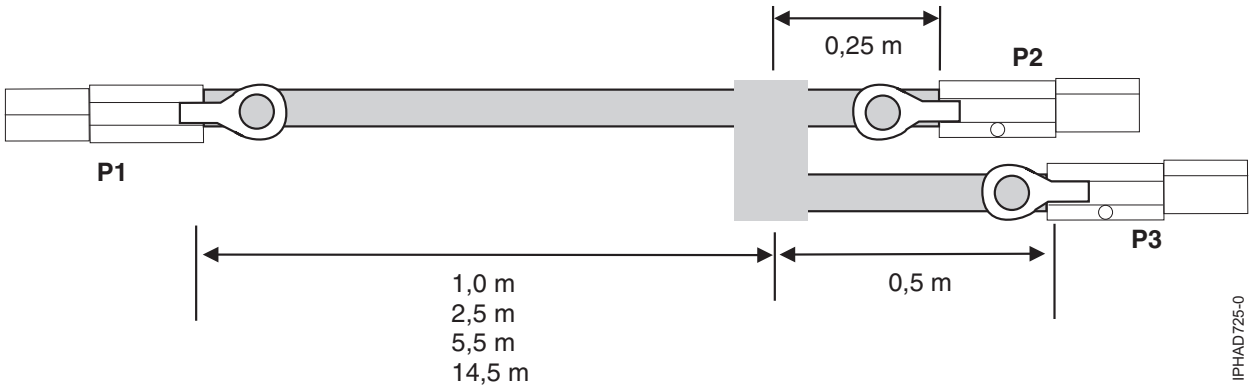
Longituds de cables de conjunt de cable YO SAS extern
